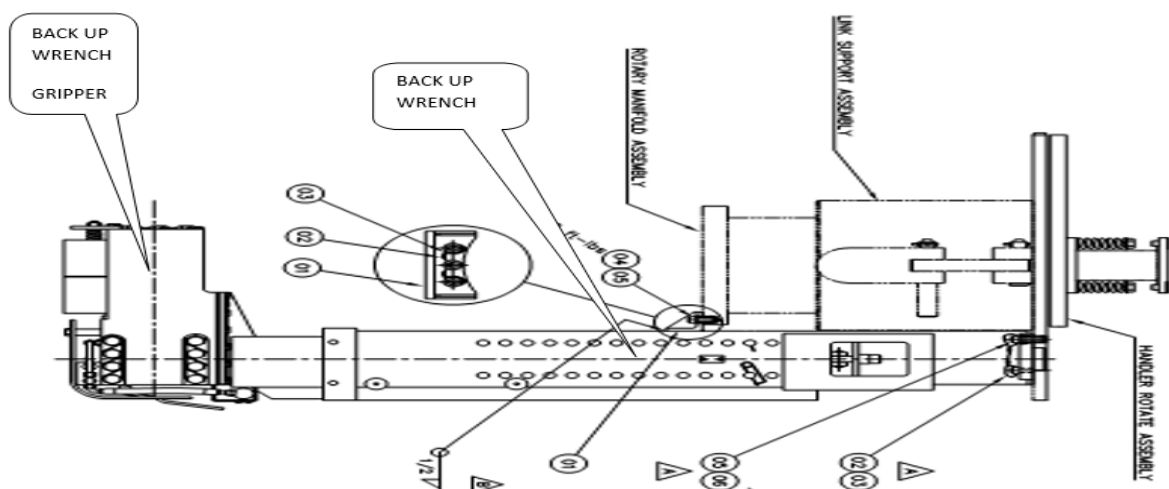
Ensemble Back-up Wrench et le Rotary Manifold [21]
